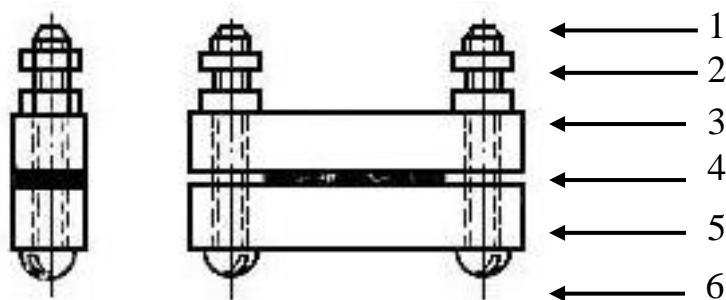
Зажим для конструктивного сжатия амортизатора и фиксации габаритного размера образца: 1 – гайка; 2 – калиброванный упор; 3,5 – зажимные планки; 4 – образец; 6 – болт
